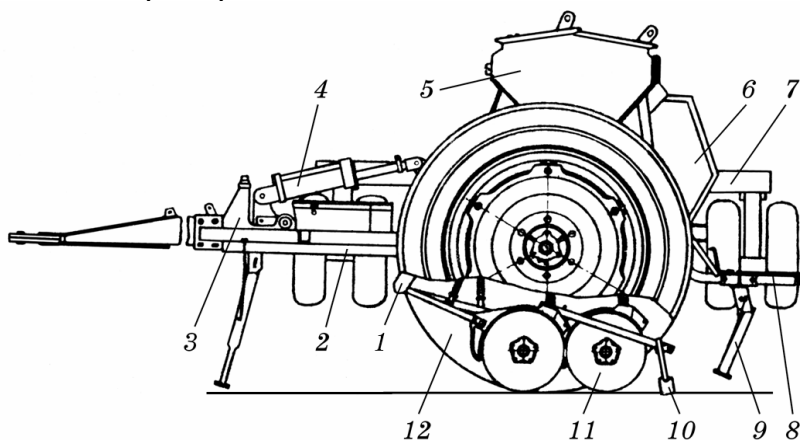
Зернотукова сівалка СЗ-5,4:
